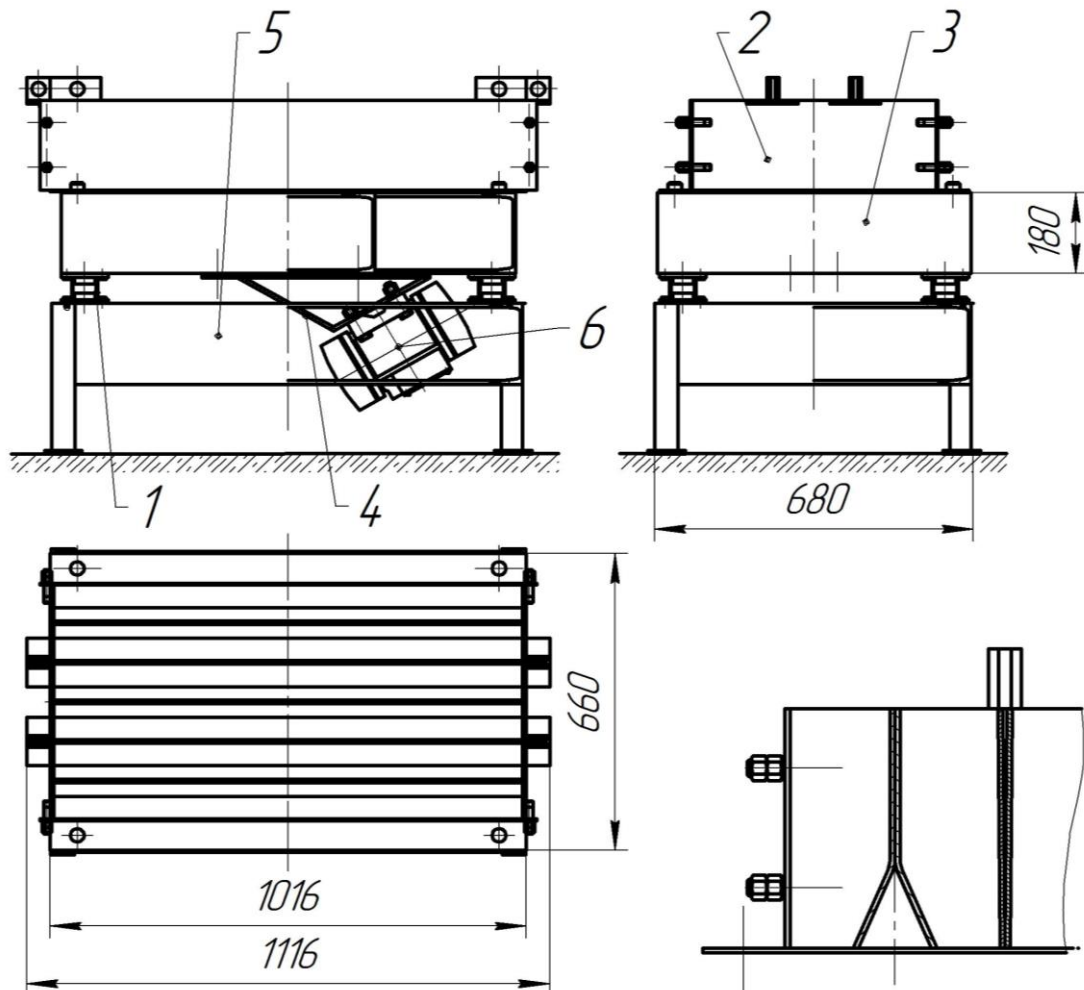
Установка для виготовлення бордюрного каменю та тротуарної плитки: 1 – віброопора; 2 – форма; 3 – рухома рама; 4 – під-вібраторна плита; 5 – основа (нерухома рама); 6 – віброзбуджувач.
